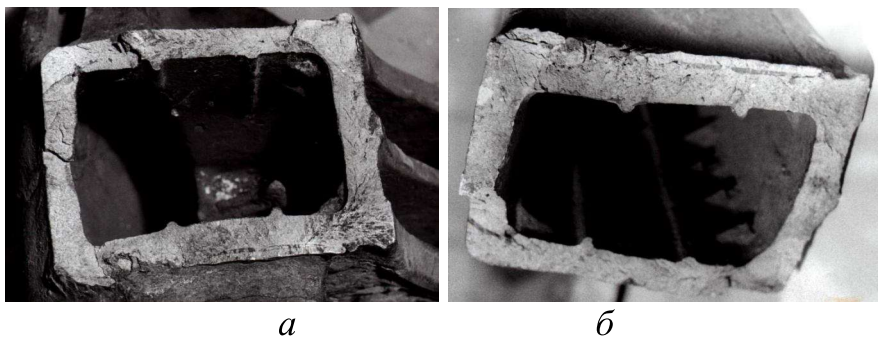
Поверхность излома корпуса автосцепки: *а* – со стороны головки; *б* – со стороны хвостовика
